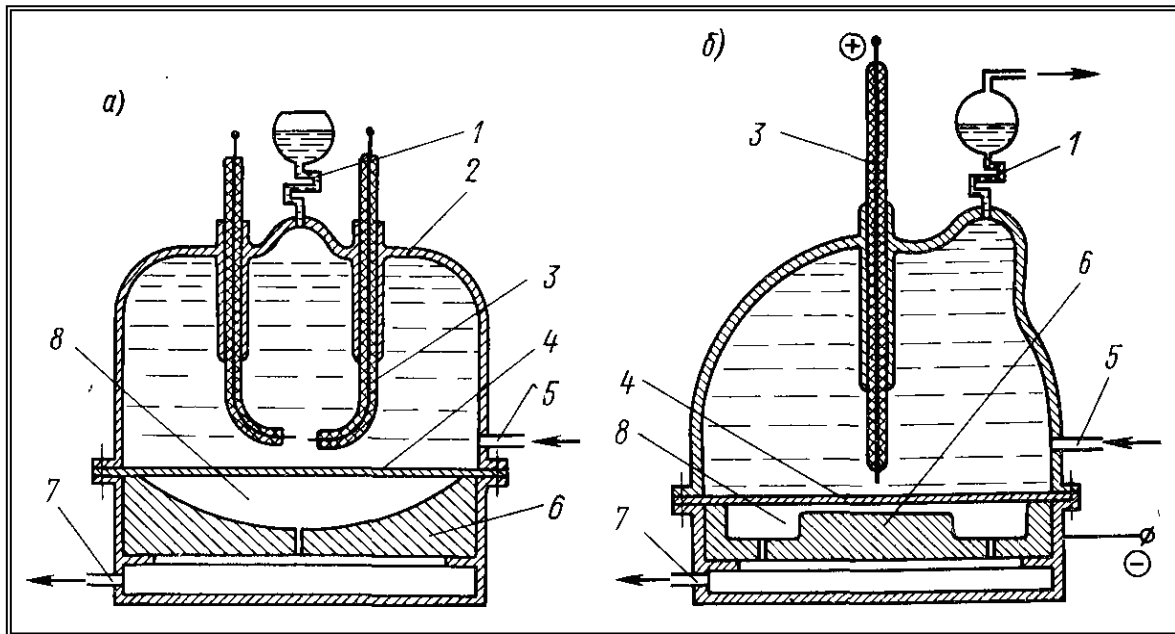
Влаштування для електрогідравлічної штамповки з двома (а) і одним (б) електродами: 1 – тормозний канал з ресивером; 2 – литий корпус влаштування; 3 – електроди; 4 – штампуємий лист; 5 – подача води; 6 – матриця; 7 – патрубок вакуумного насосу; 8 – вакуумована порожнина
